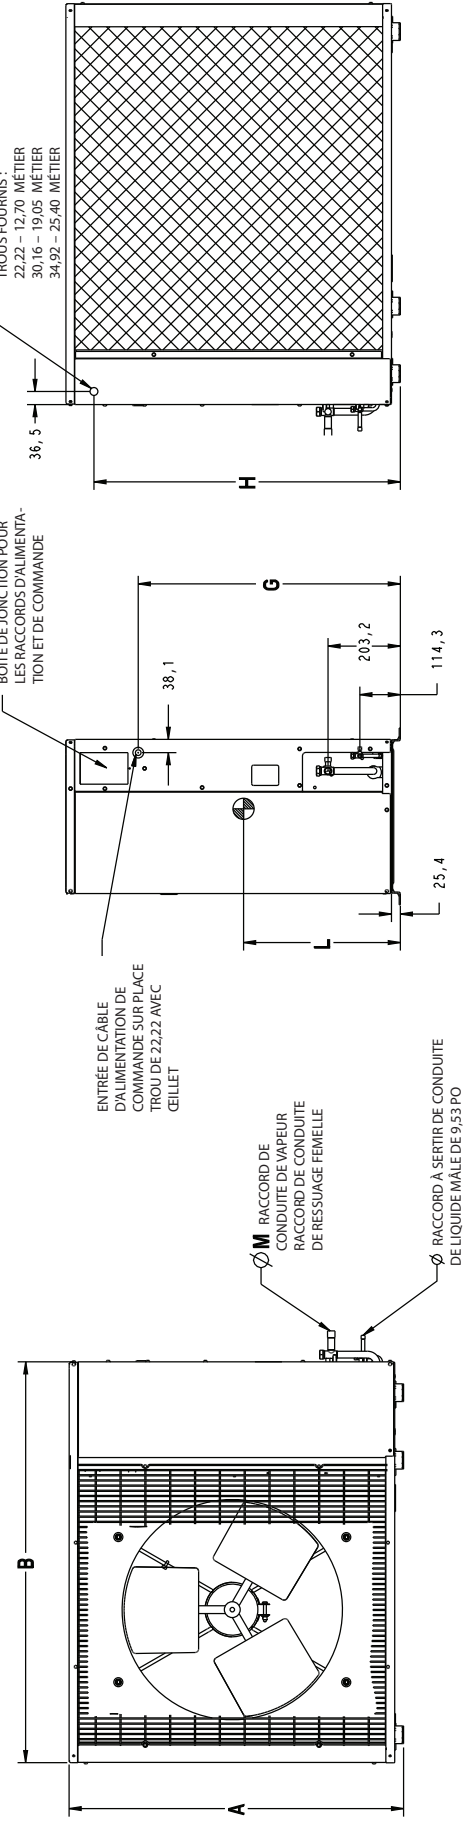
Dimensions de l'appareil extérieur 38QRR - SI
